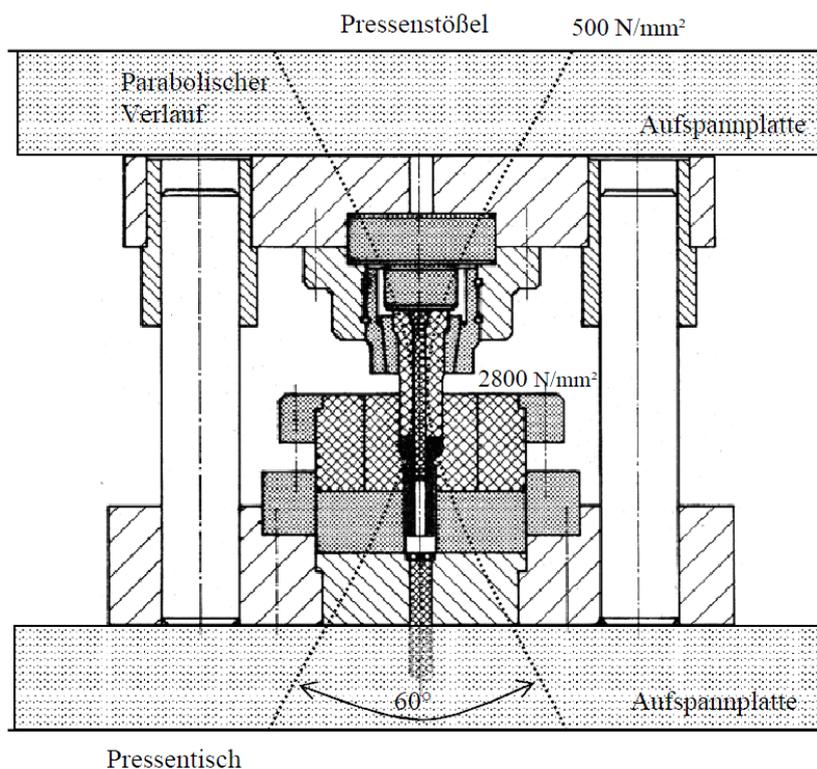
Kraftverteilung in einem Fließpresswerkzeug mit Aufspannplatte zur Verminderung der Flächenpressung auf
